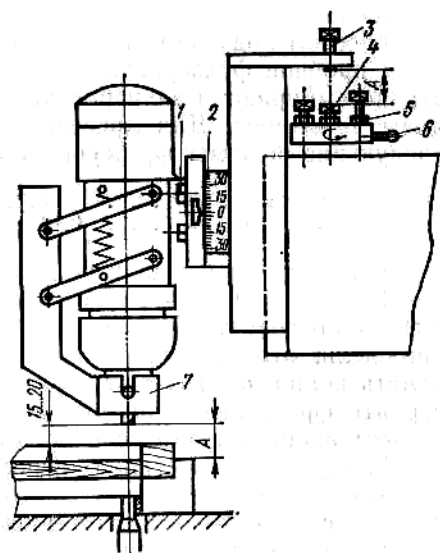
Настройка ограничителей хода суппорта фрезерного станка:
